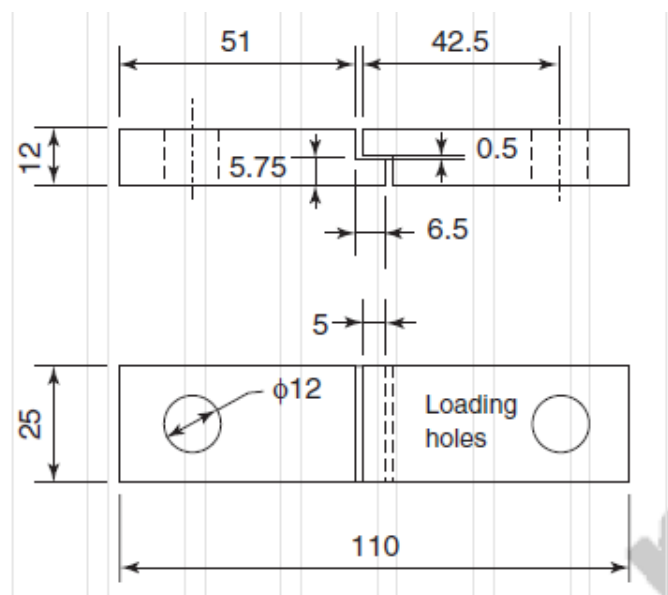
Dimensões do provete para ensaio de tração de juntas sobrepostas [1]
